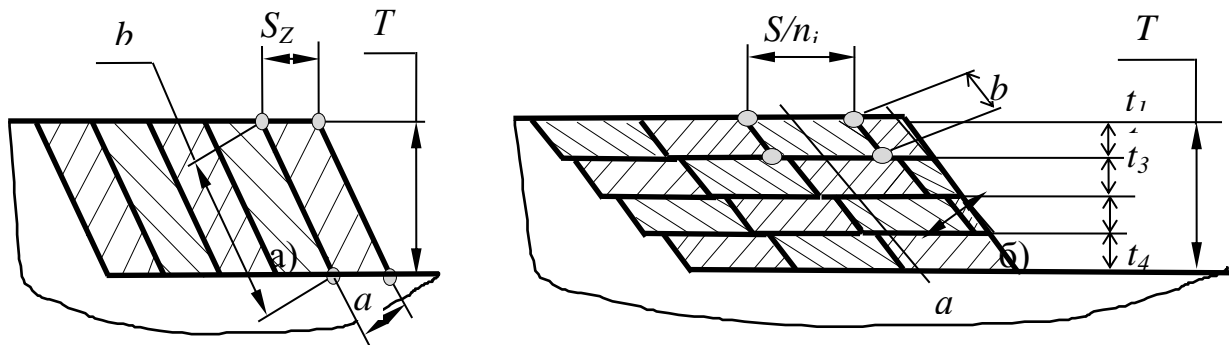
Схеми різання торцевими фрезами з розподілом припуску:
